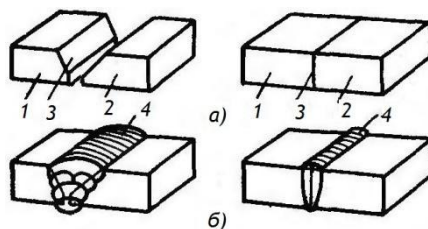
Соединение деталей сваркой плавлением, где а – перед сваркой, б – после сварки; 1, 3 – свариваемые детали, 2 – оплавляемые кромки, 4 – сварной шов
